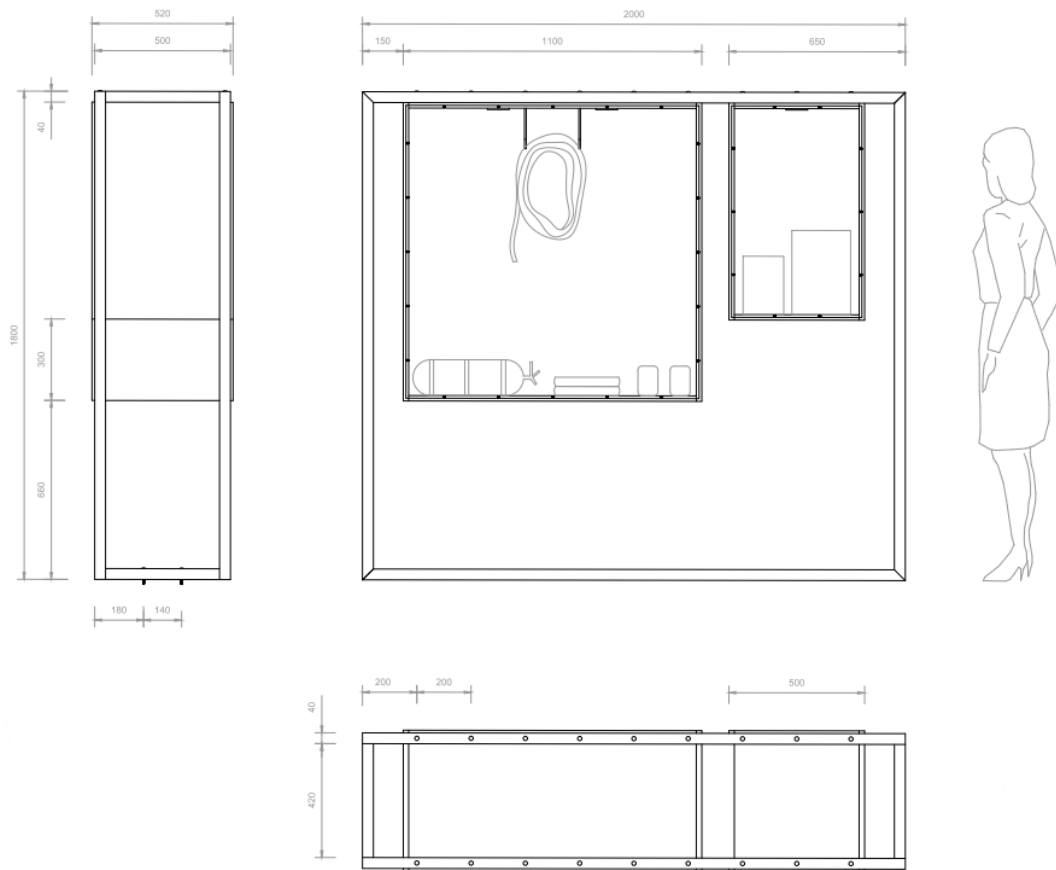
Desenho de conjunto do equipamento. Fonte: Autor.
